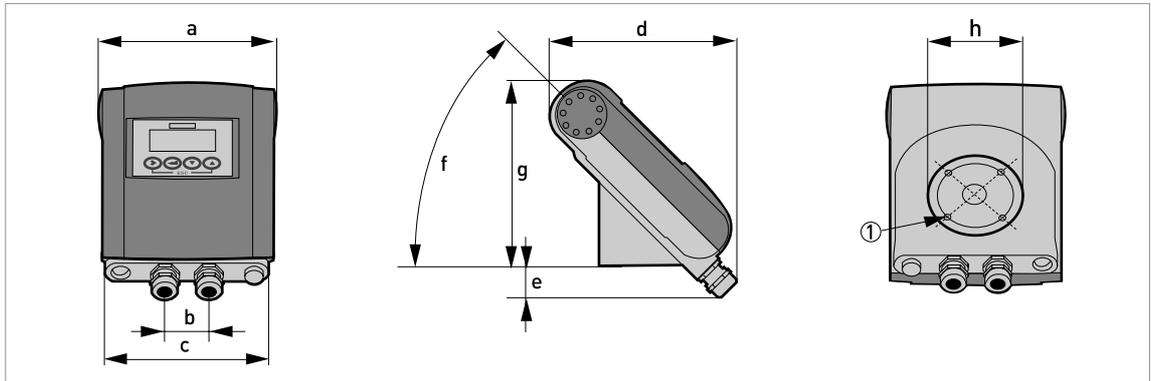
Dimensions de la version 45° compacte, boîtier en aluminium
